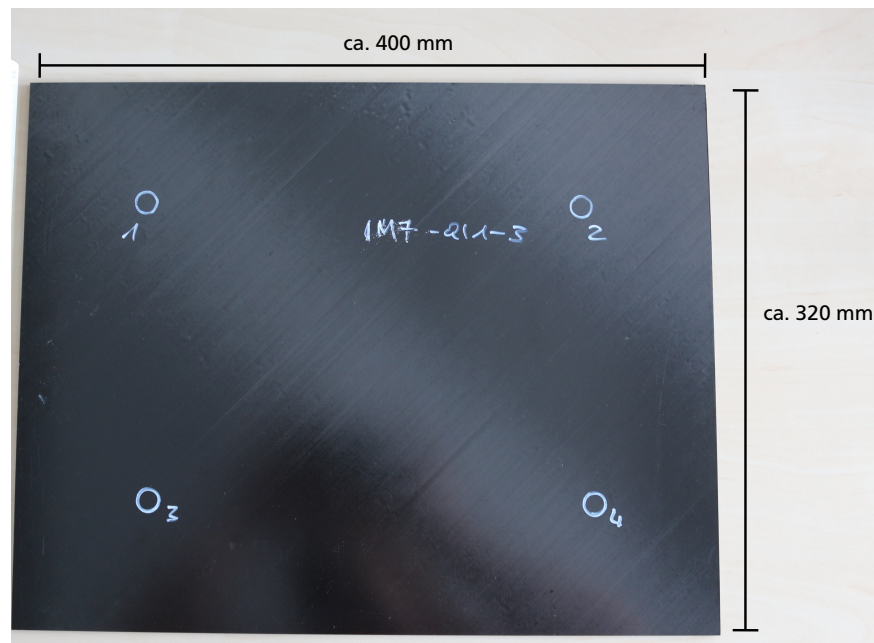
Die auf der Ausgangsplatte gewählten Positionen für die Dickenmessung sind mit einem weißen Kreis markiert.
